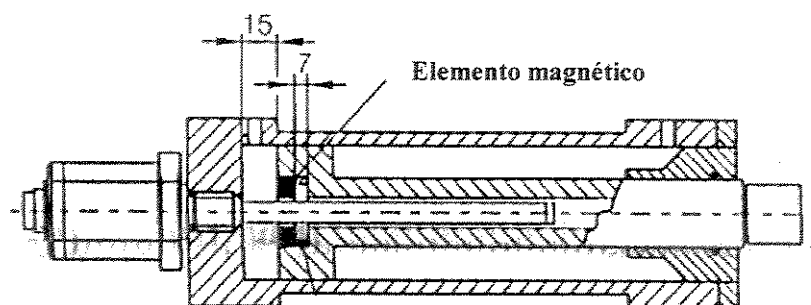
Sensor de posição montado no cilindro hidráulico.
